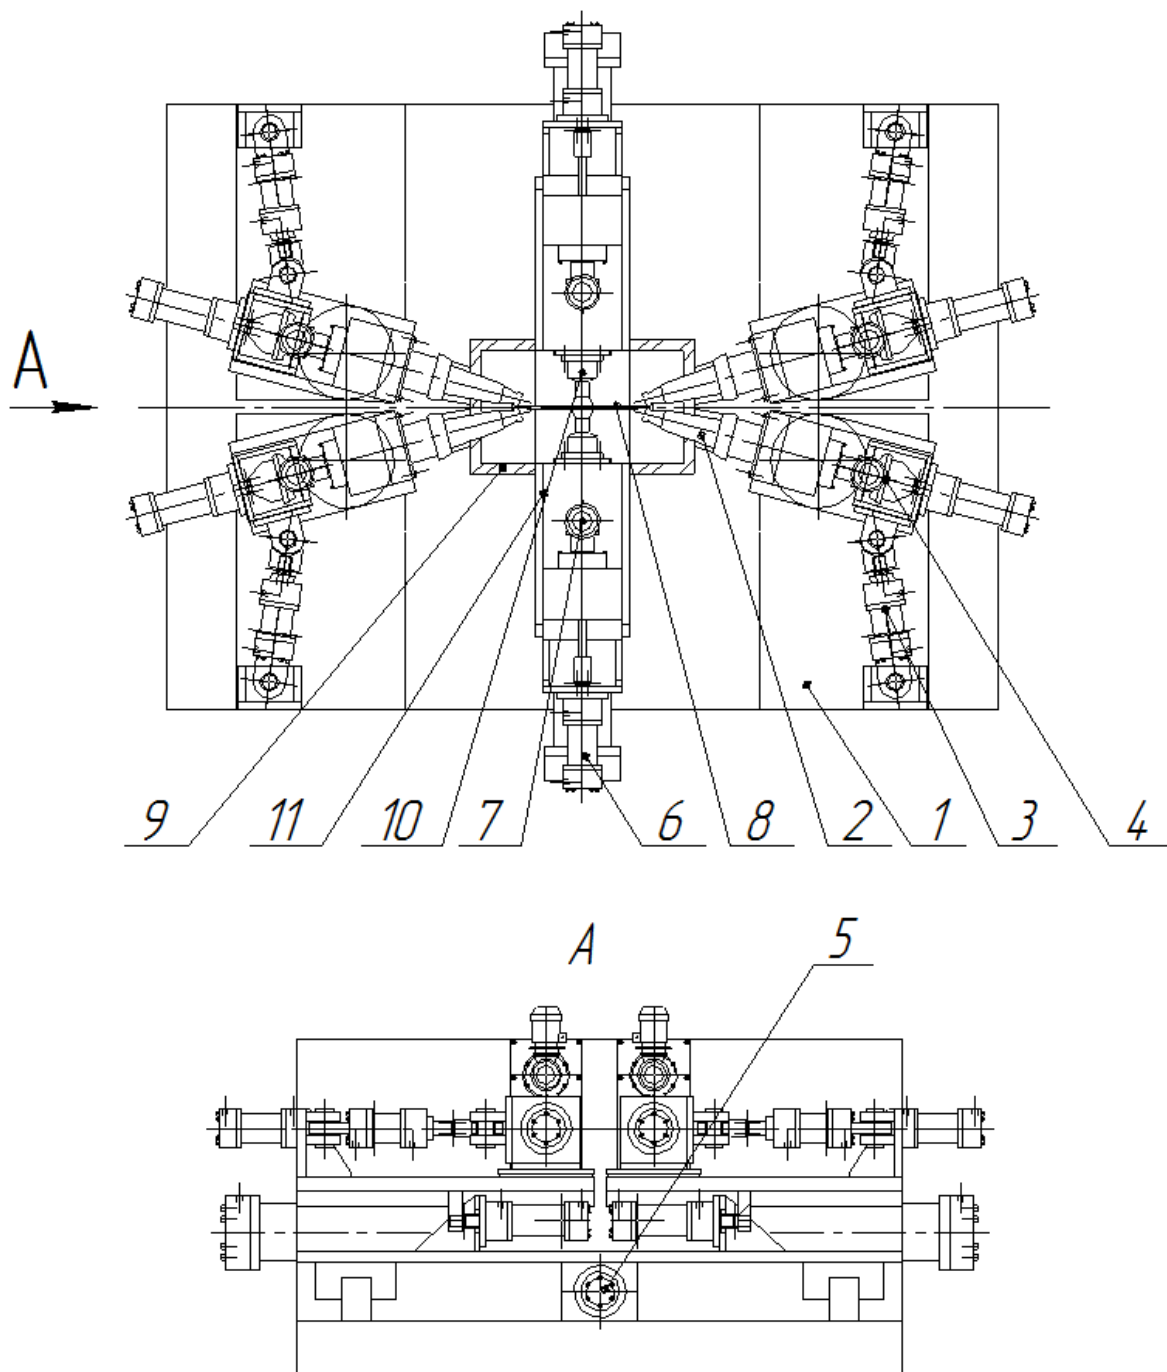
Общая схема конструкции оборудования для изотермической раскатки заготовок типа «диск»
